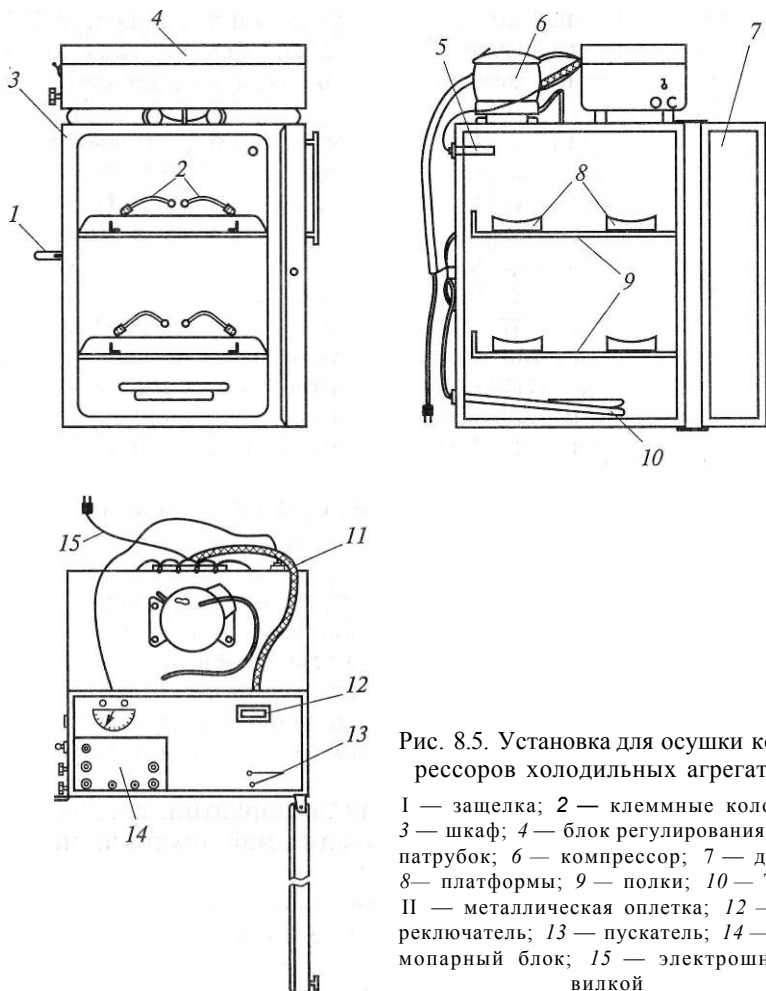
Установка для осушки компрессоров холодильных агрегатов:
